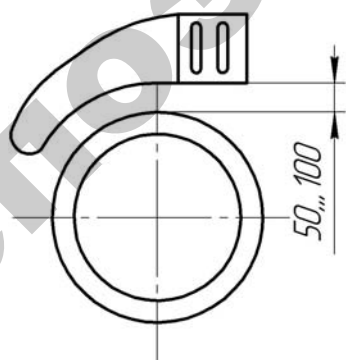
Установка зазора между ребровой подбирающего барабана и направляющими
